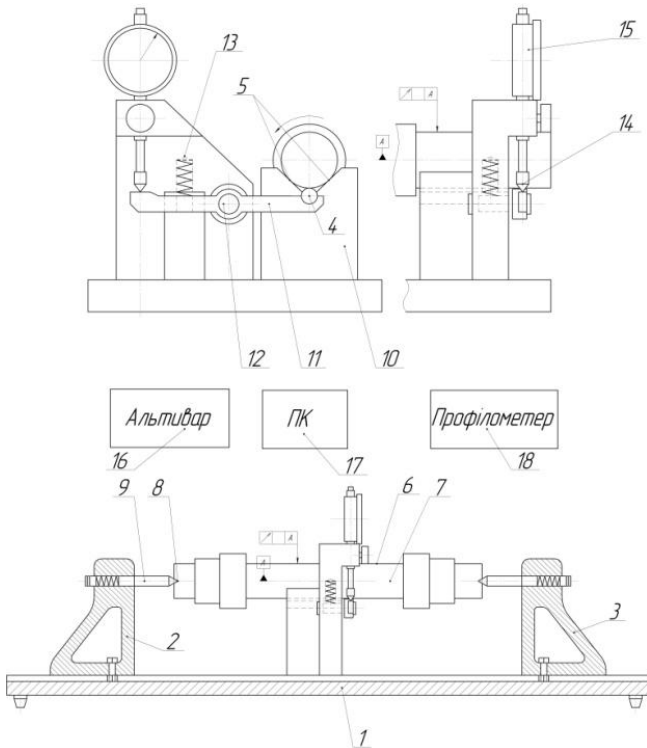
Багатомірний пристрій для контролю ступінчастих валів
